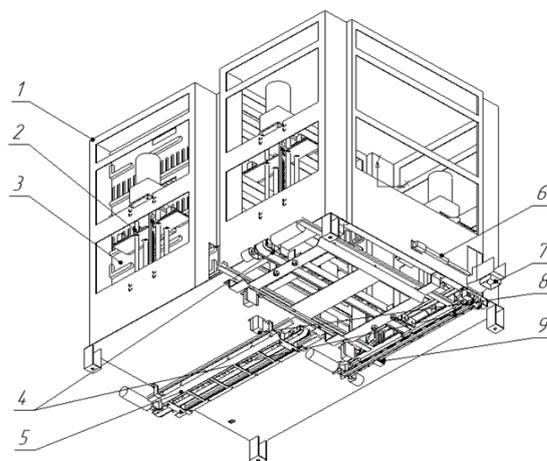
Устройство подачи рассады для посадочной машины: 1 — корпус устройства; 2 — подъемный механизм; 3 — контейнер; 4 — линейные приводы, предназначенные для разгрузки контейнера; 5 — линейный привод, перемещающий контейнеры; 6 — актуаторный привод заслонки контейнера; 7 — выход для рассады и направляющих; 8 — электромеханический замок; 9 — актуаторный подъемный механизм привода
